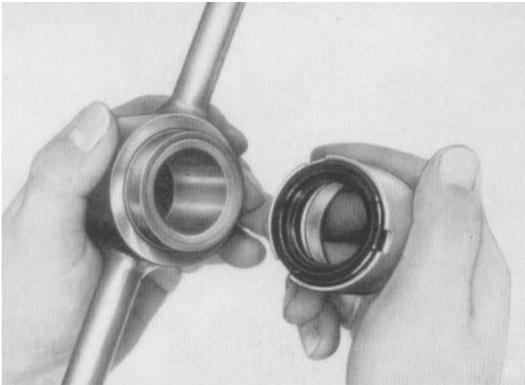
Kombierter Montageschlüssel zum Eindrücken des Dichtringes in den Gewinding
